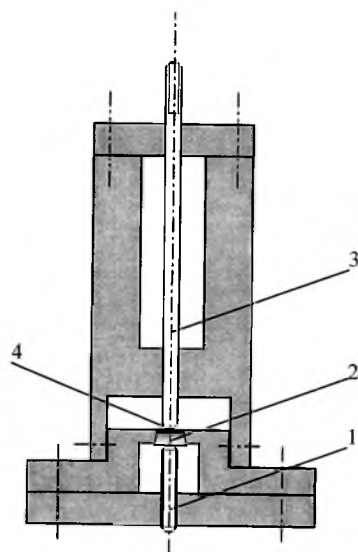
Схема устройства для пайки металлического стержня к поверхности алмаза: 1 – поджимной штифт; 2 – кристалл алмаза; 3 – стержень; 4 – пластинка припоя.
